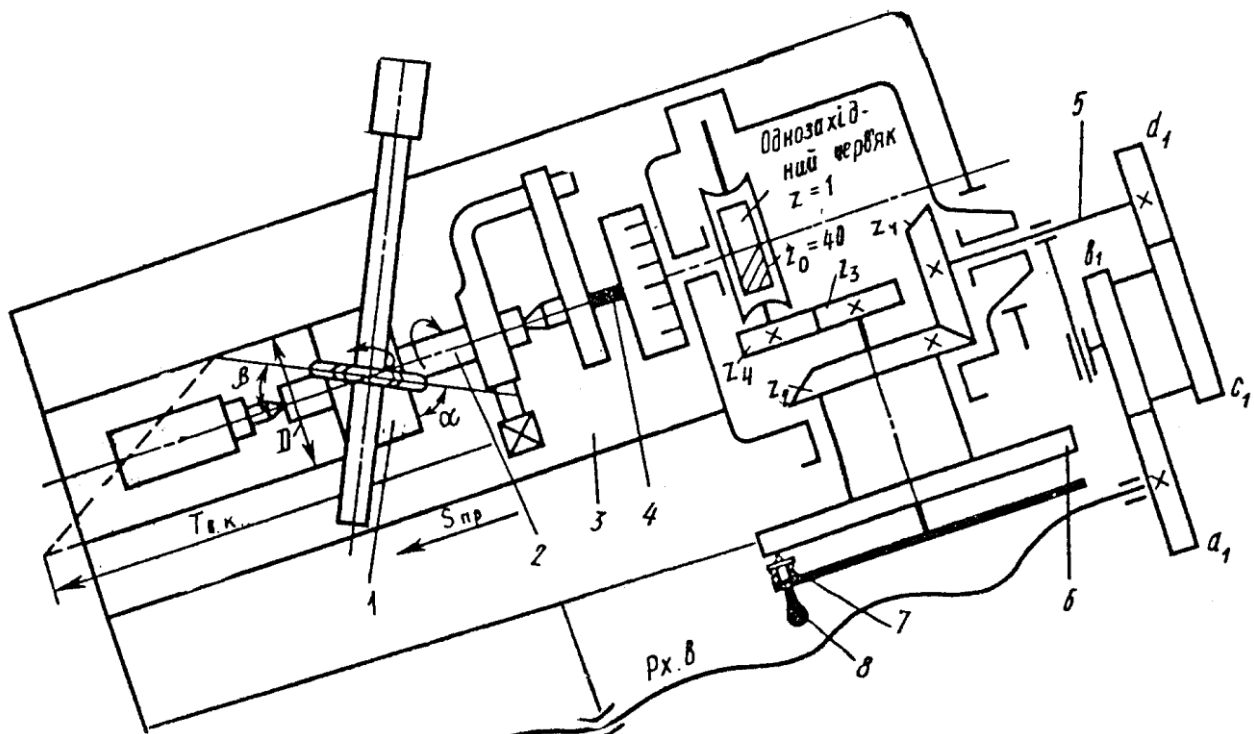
Схеми налагоджування універсально-фрезерного верстата та ділильної головки для фрезерування гвинтових канавок
